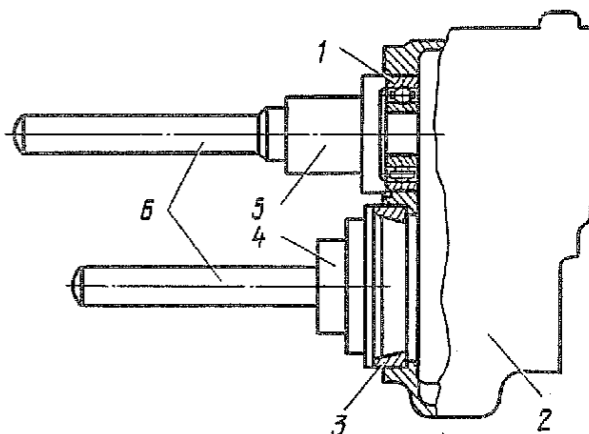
Запрессовка наружных подшипников колесного редуктора:
